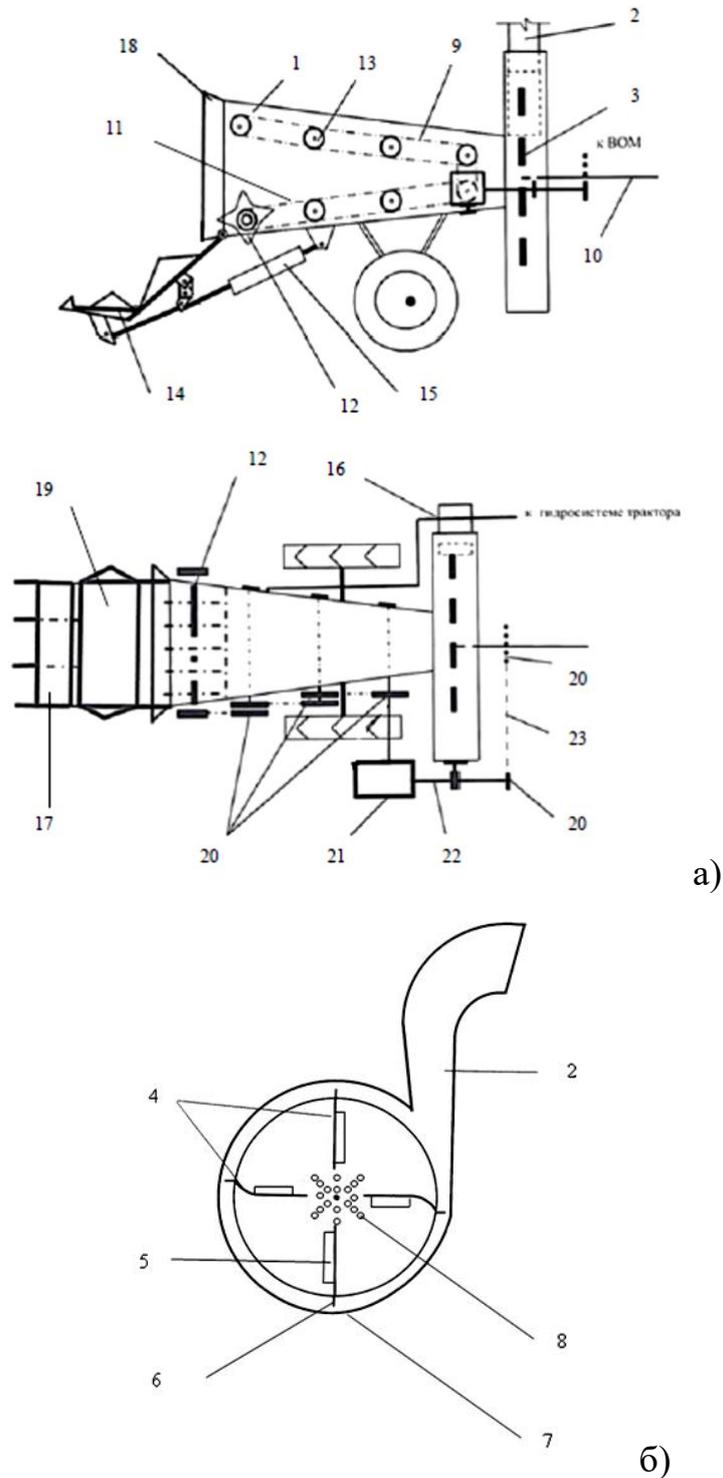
Конструктивная схема рубильной машины: а) - общий вид; б) - кожух рубительной машины с отверстиями и измельчитель с лопатками, с установленными на их поверхностях ребрами
